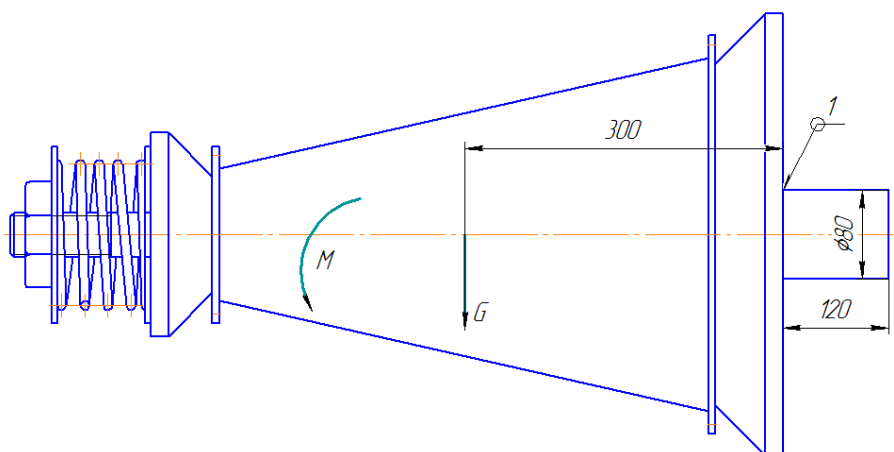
Схеми для розрахунку кутового шва за умови дії на нього згинального моменту
